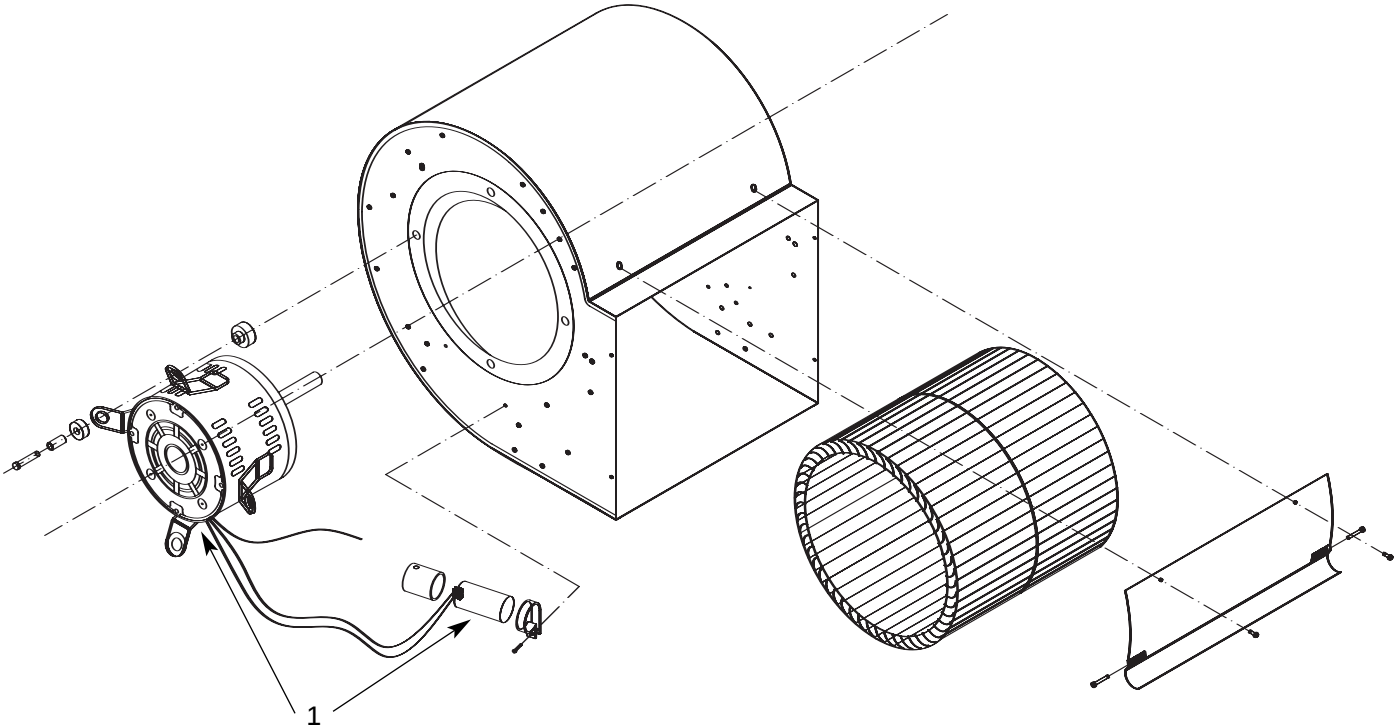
Illustration des pièces détachées pour soufflantes à commande directe
